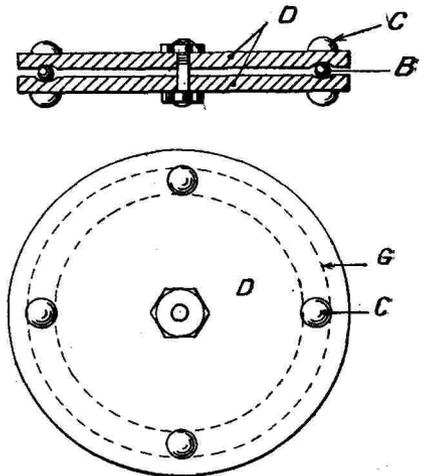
Support d'orientation pour poste portatif vu en coupe et en plan.
